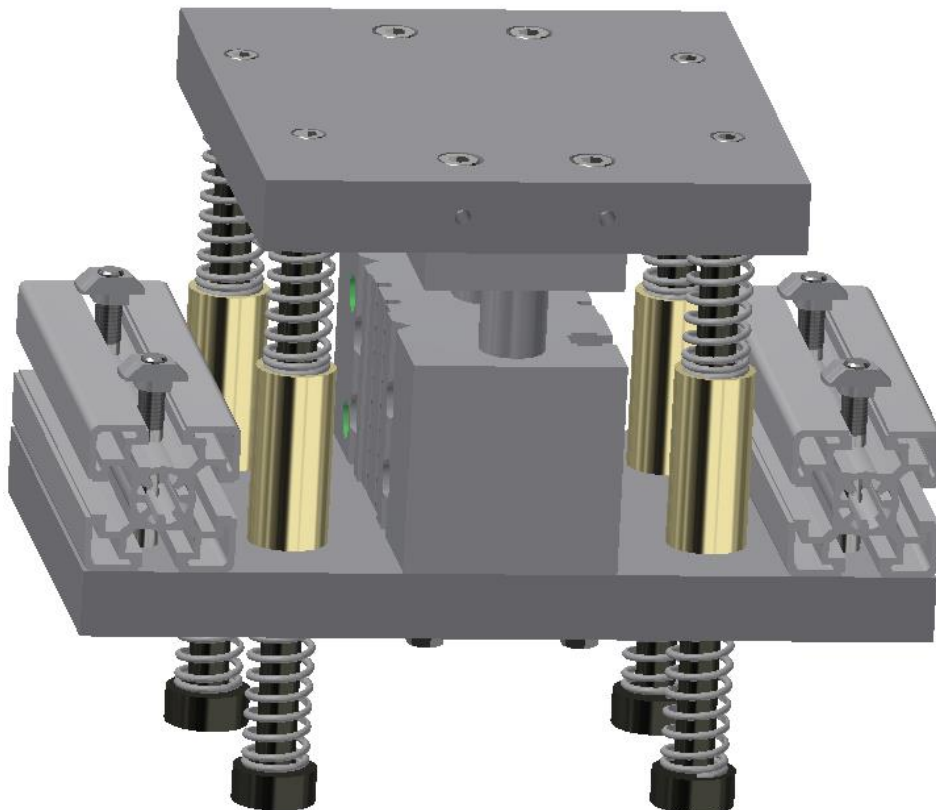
Pohled na sestavu bez podélné dráhy [autor]
